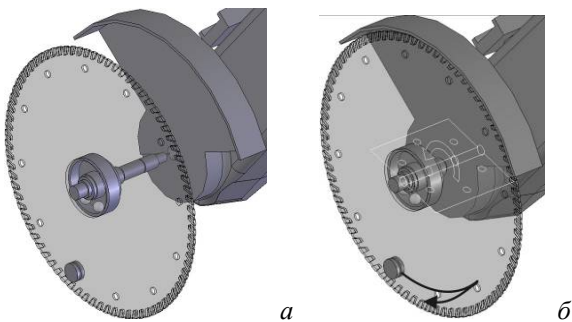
Встановлення вала з деталями у корпус РШМ: а – геометричне з'єднання; б – перевірка
